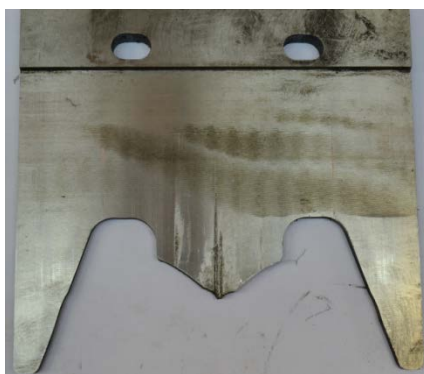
Общий вид отрубного устройства со стандартным типом штампа
